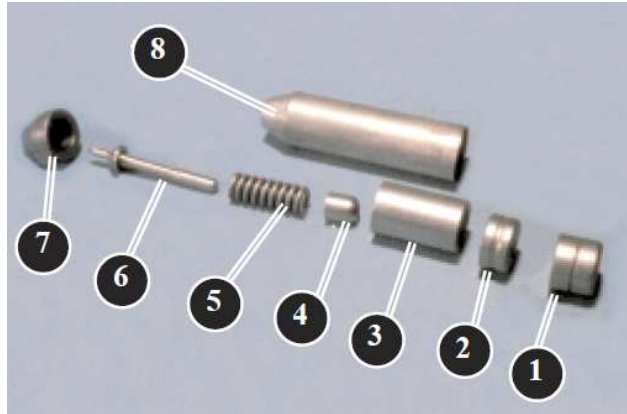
Componentes del inyector de cápsula DI.
